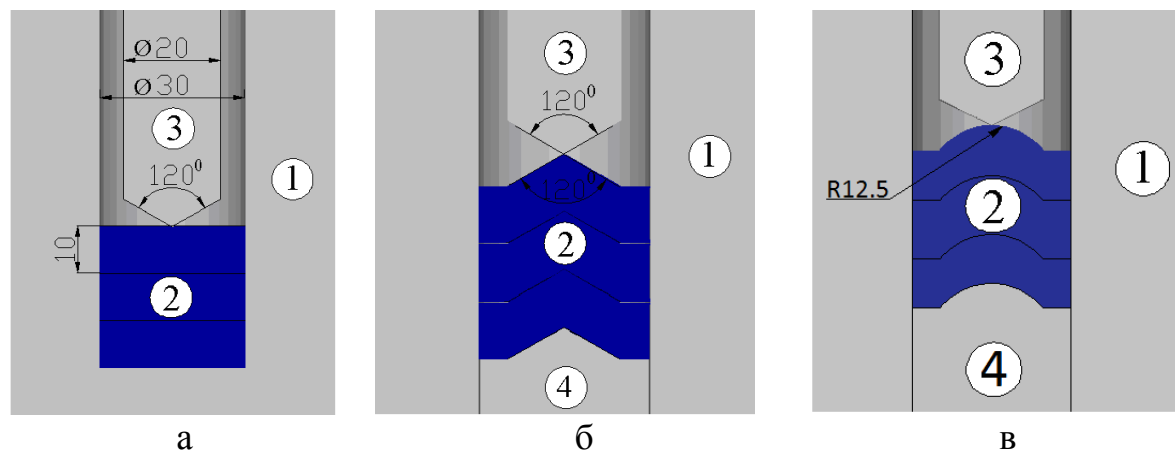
Схемы сквозной прошивки заготовок с торцами: плоскими (а), с коническими (б) и со сферическими (в)
